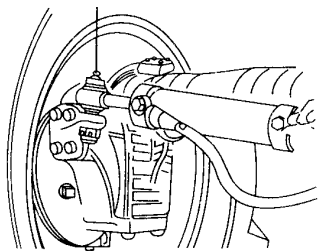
Смазка шарниров гидроцилиндра ГОРУ
